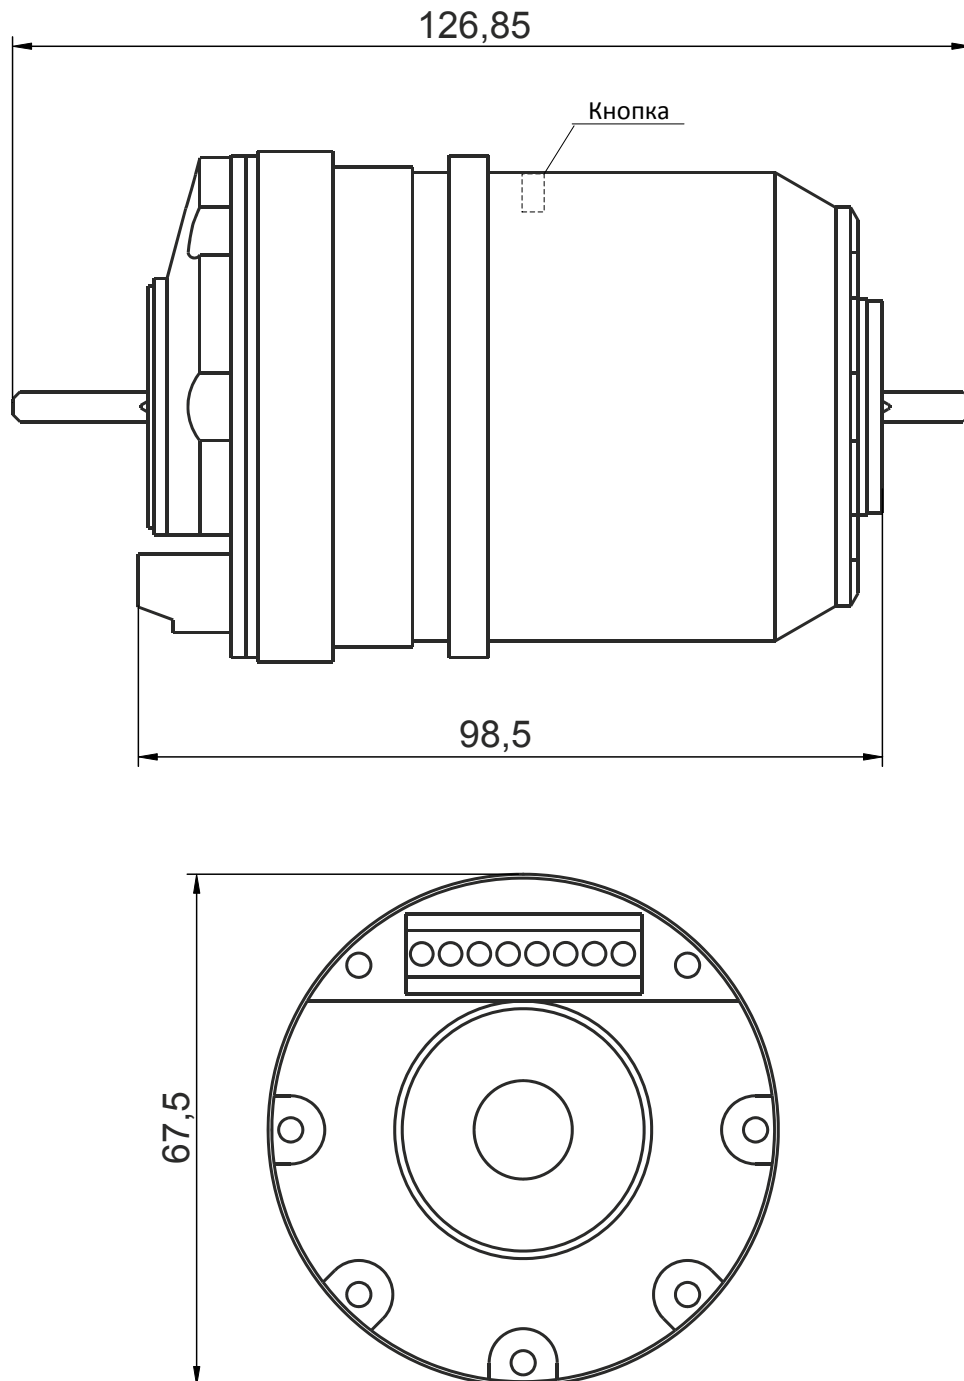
Габаритные размеры датчика положения привода ДП-3/2.
